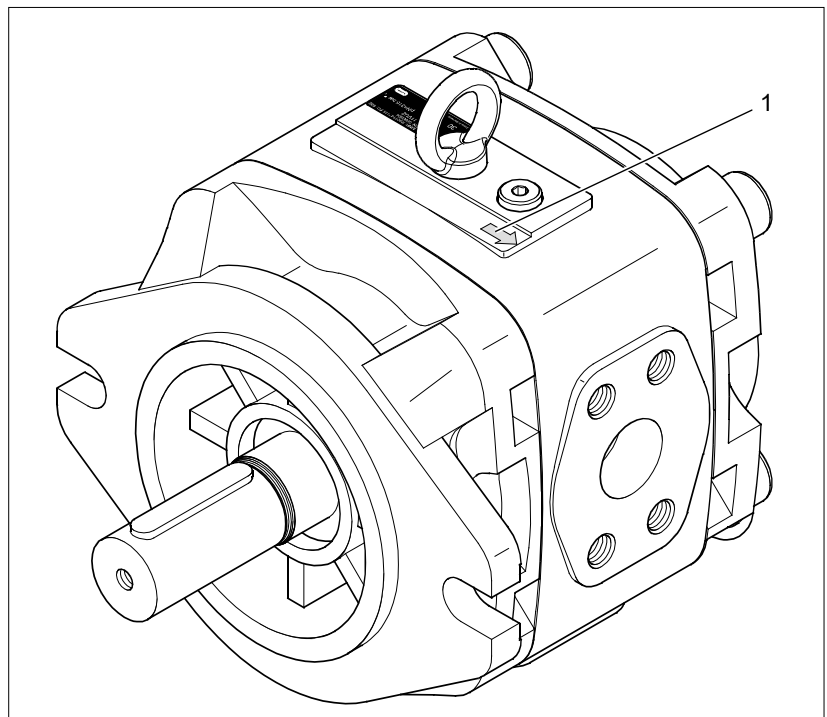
Montage Innenzahnradpumpe PGH.-3X
